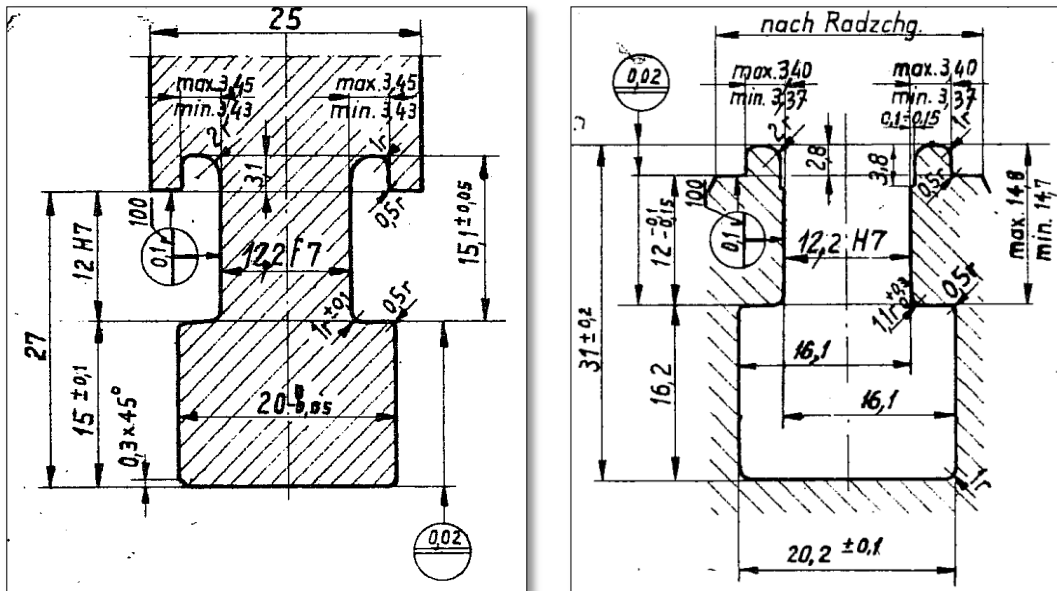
dimensioni del piede palare e della cava sul disco del 7° stadio della turbina n° 3.
